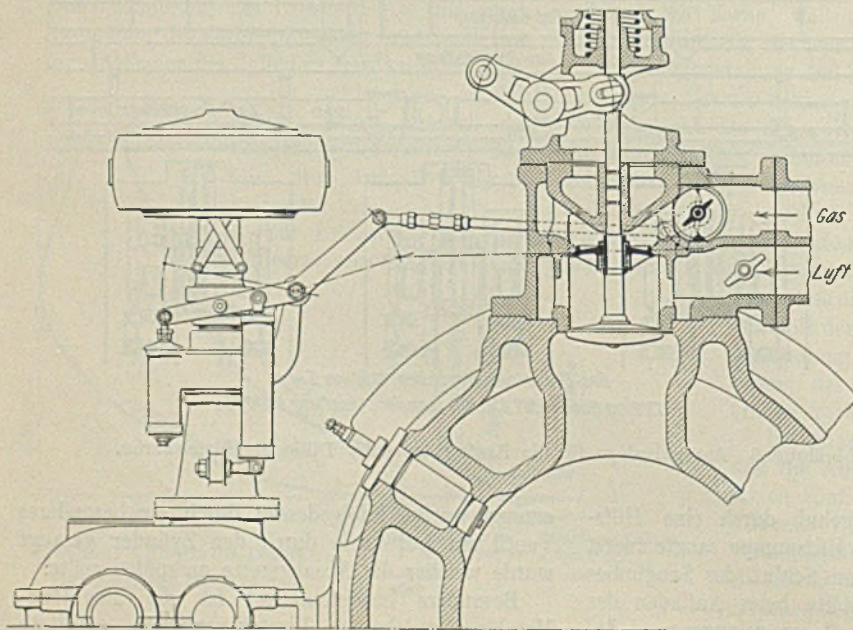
Einlaßventil für Gasmaschinen mit Ausspülung, Bauart Ehrlardt & Schmer.
